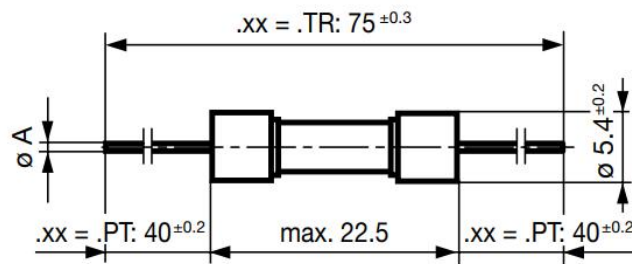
Габаритні розміри запобіжника 0001.1014.PT
